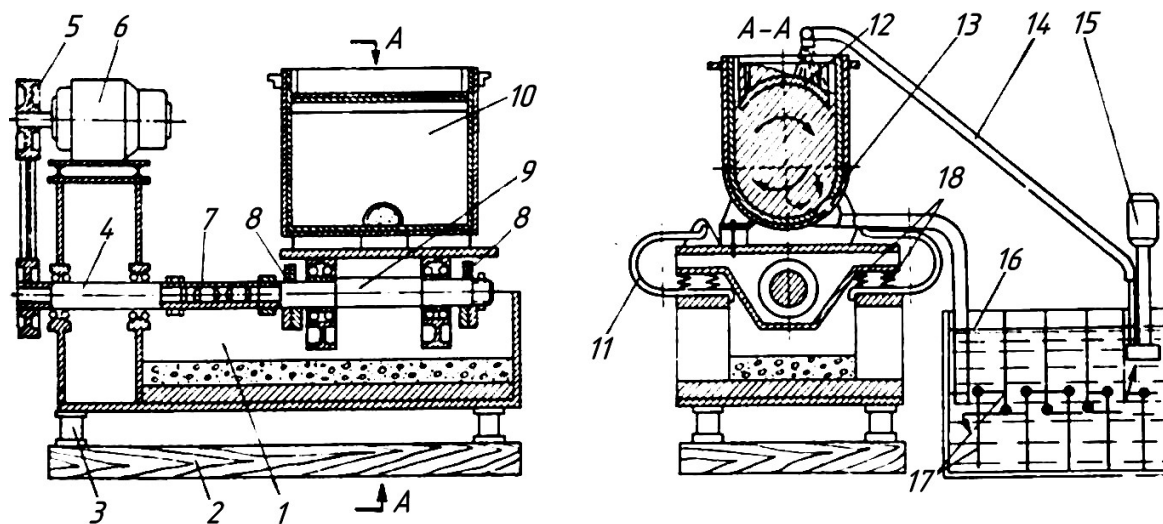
Принципиальная схема виброгидроабразивной установки с экран-вставкой: 1 – сварная рама; 2 – деревянная платформа; 3 – резиновые амортизаторы; 4 – промежуточный вал; 5 – клиноремennая передача; 6 – электродвигатель; 7 – гибкая муфта; 8 – дебалансные диски; 9 – вал; 10 – резервуар; 11 – С-образные рессоры; 12 – экран-вставка; 13 – люк; 14 – напорный рукав; 15 – электропомпа; 16 – отстойник; 17 – вертикальные перегородки; 18 – цилиндрические пружины
